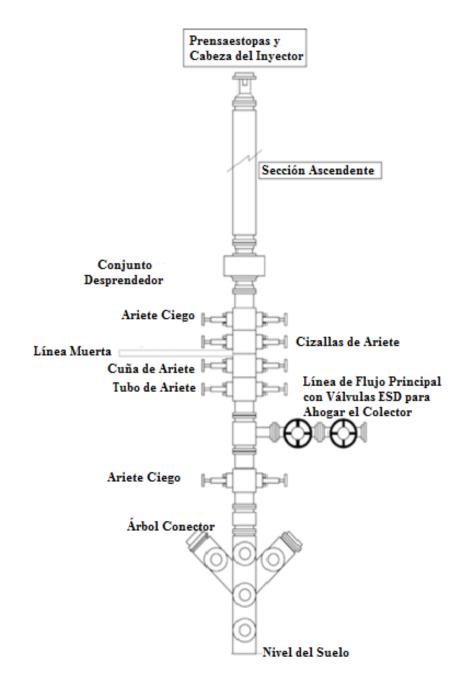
Ensamblaje típico con tubería flexible. Fuente: Leading Edge Advantage International Ltd 2002.
